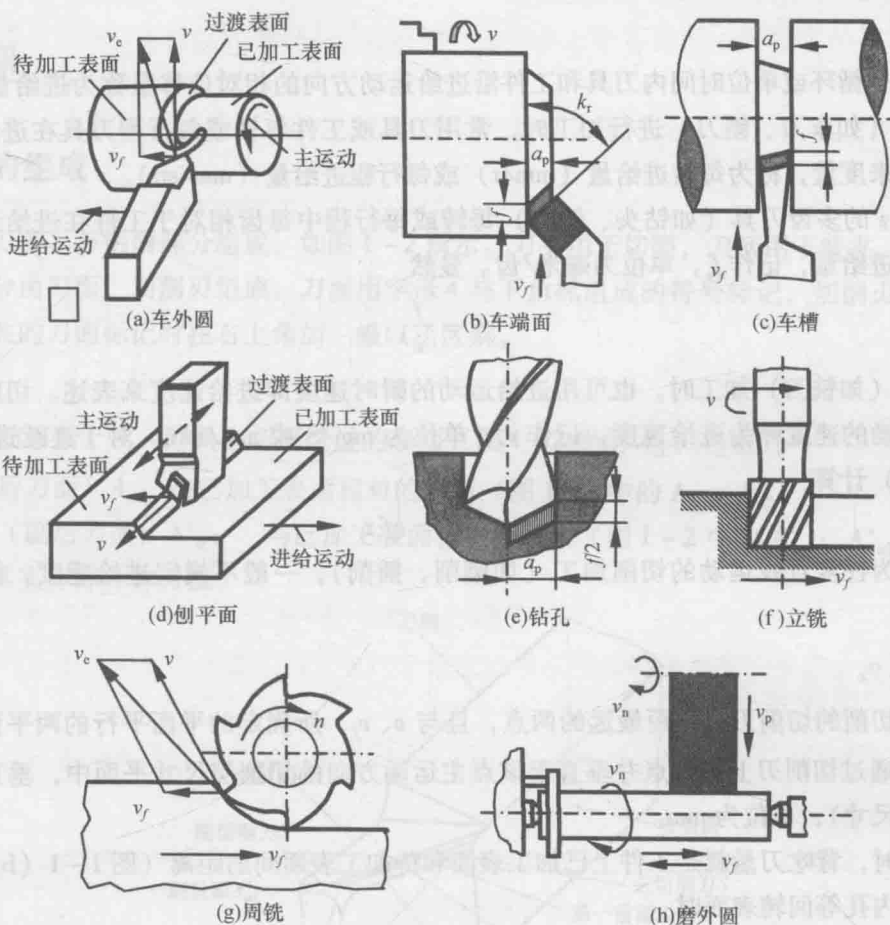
常见的加工方法的加工表面、切削运动、切削用量
